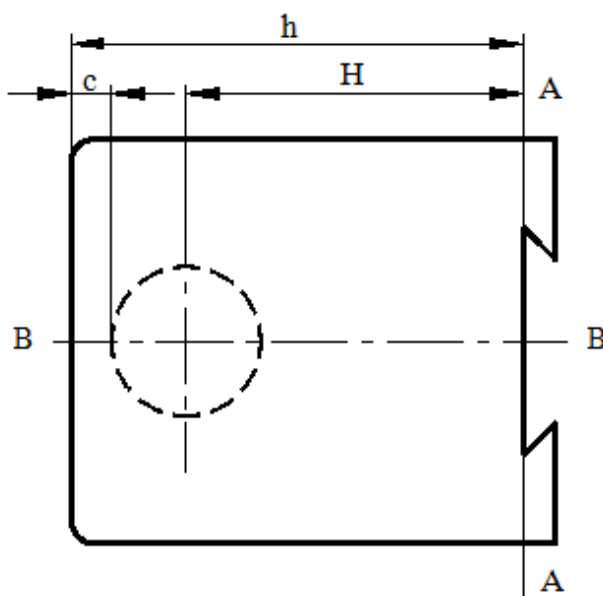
Компоновка коробки скоростей вертикально-сверлильных и вертикально-фрезерных станков
